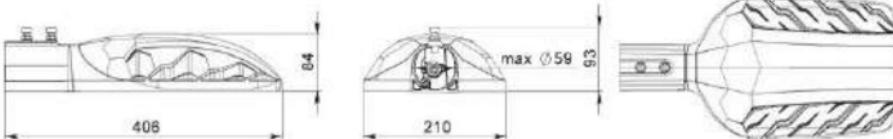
Общий вид светильника Street X1 с консольным креплением.
